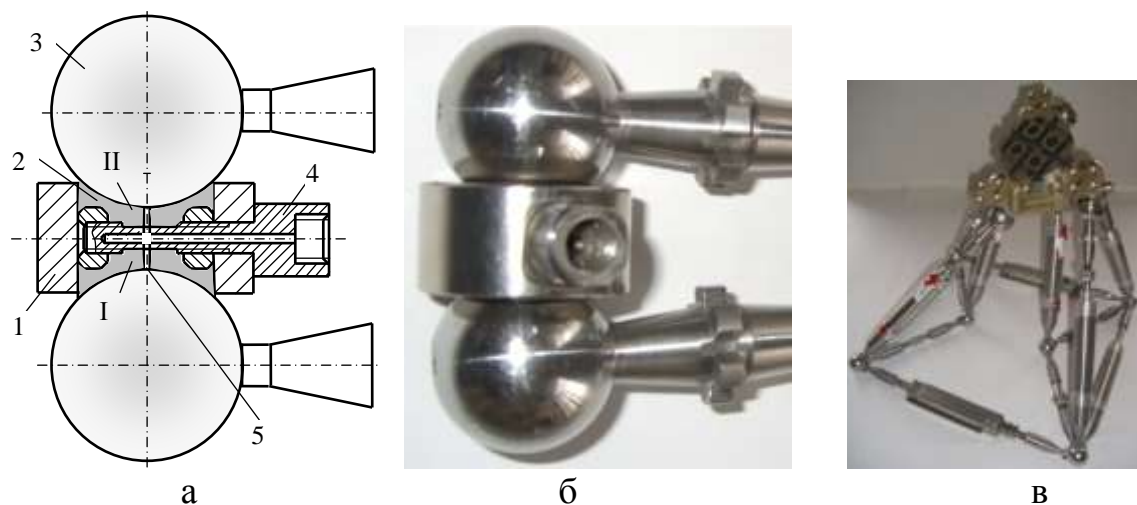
Схема подвійного аеростатичного магнітного шарніра (а), виготовлений дослідний зразок (б) та система із розробленими шарнірами (в)
